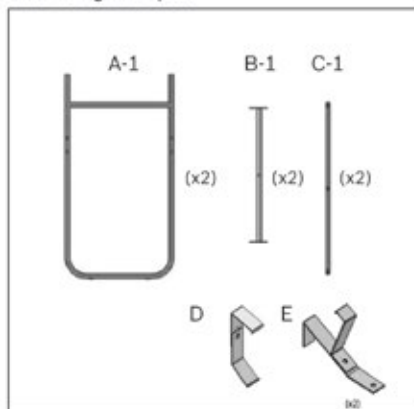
Vista del conjunto de componentes incluidos para el soporte ensamblados
